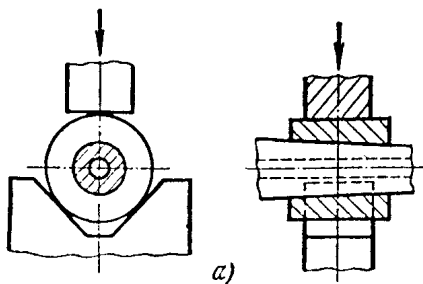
Схема протяжки пустотелой заготовки на оправке:
